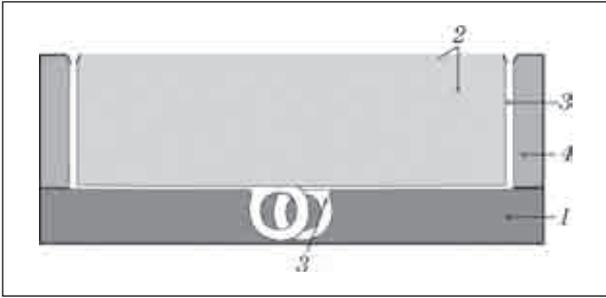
Схема ливарної форми верхнього кільця із ручками: 1 — підставка; 2 — ливарний стрижень; 3 — воскова модель кільця; 4 — стінки форми
